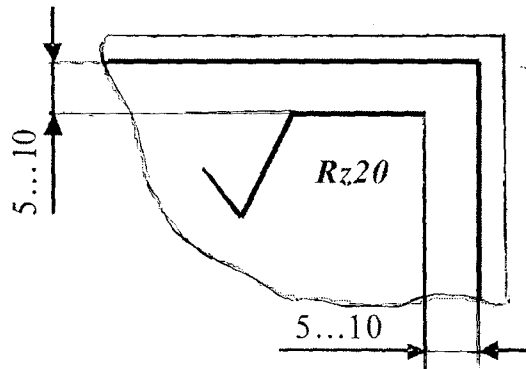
Примеры простановки знаков для обозначений требований к шероховатости
